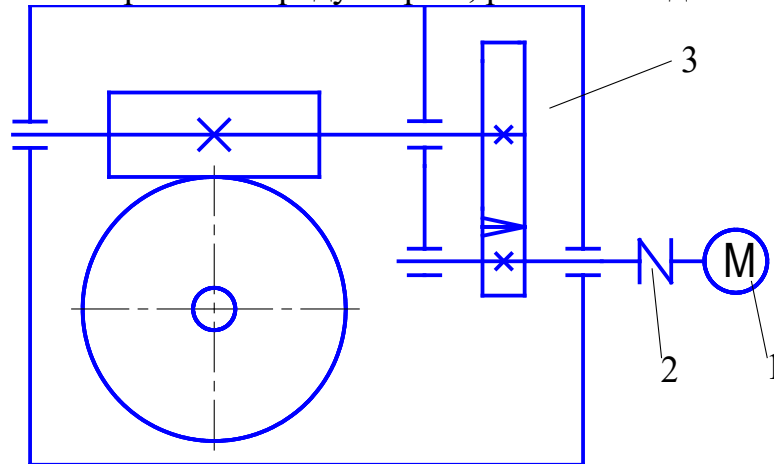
Кинематическая схема привода с зубчато-червячным редуктором
